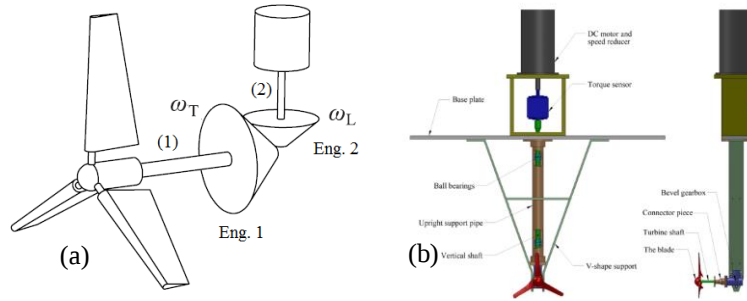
(a) Modelo esquemático do sistema de engrenagem cônica | (b) THC de eixo horizontal que utiliza engrenagem cônica desenvolvida por Bibeau et al. (2015).
